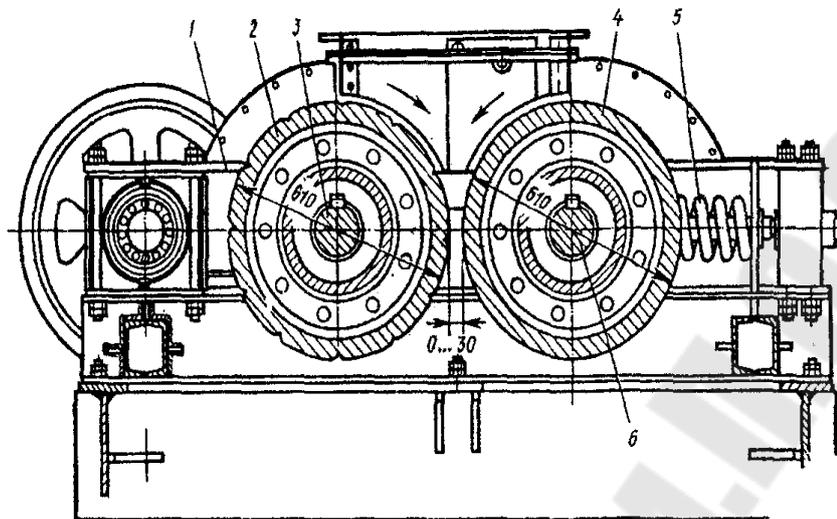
Общий вид валковой дробилки: 1- станина; 2,4- параллельные цилиндрические валки, вращающиеся на встречу друг другу; 3,6- подшипники; 5- пружинная опора
